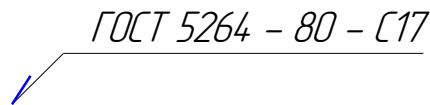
Структура обозначения шва сварного соединения:
